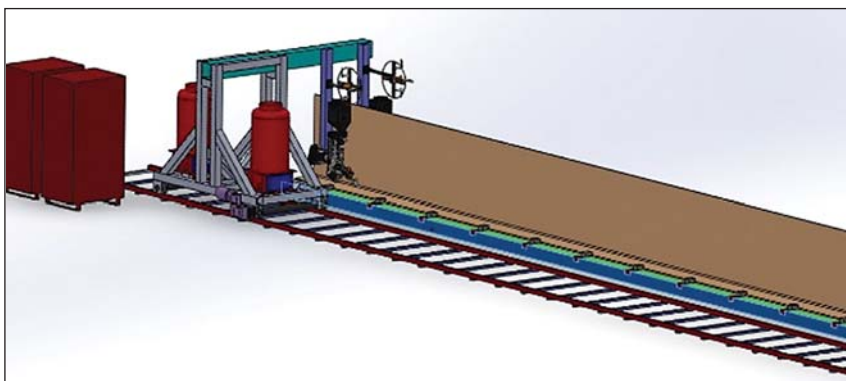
Автоматизированная линия сборки и сварки тавровых балок
